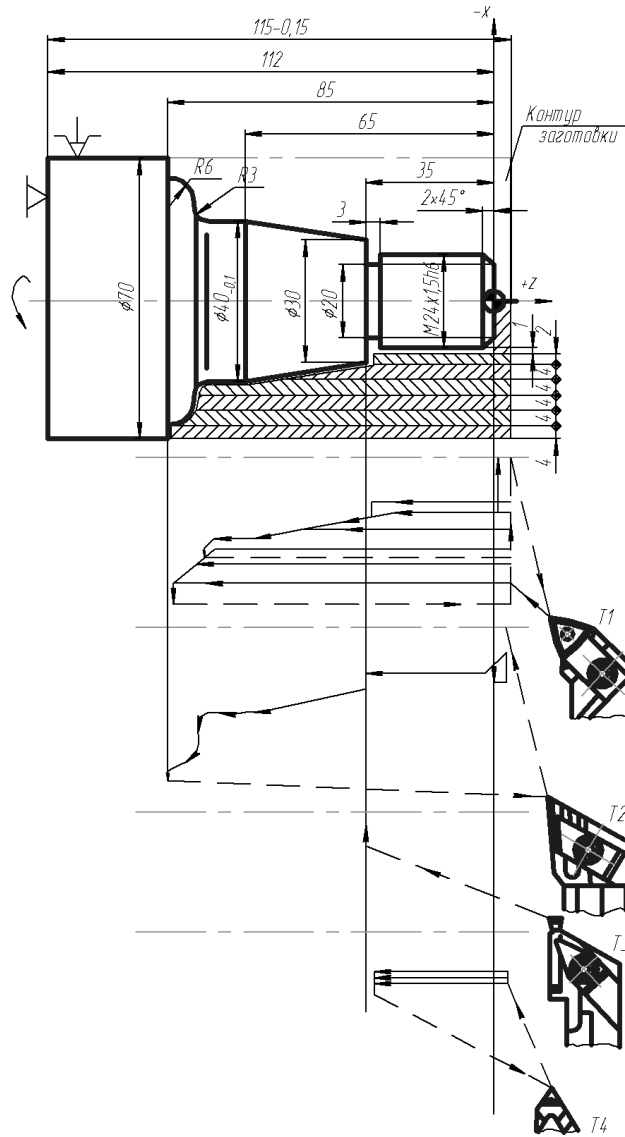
Схема обробки деталі «Валик різьбовий»
